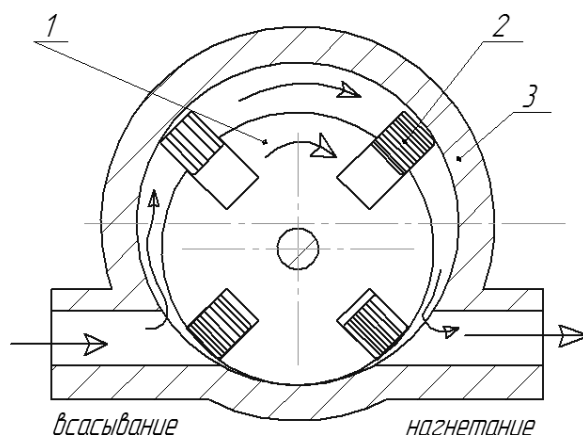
Пластинчатый насос: 1 – ротор; 2 – лопатки (пластины); 3 – статор
